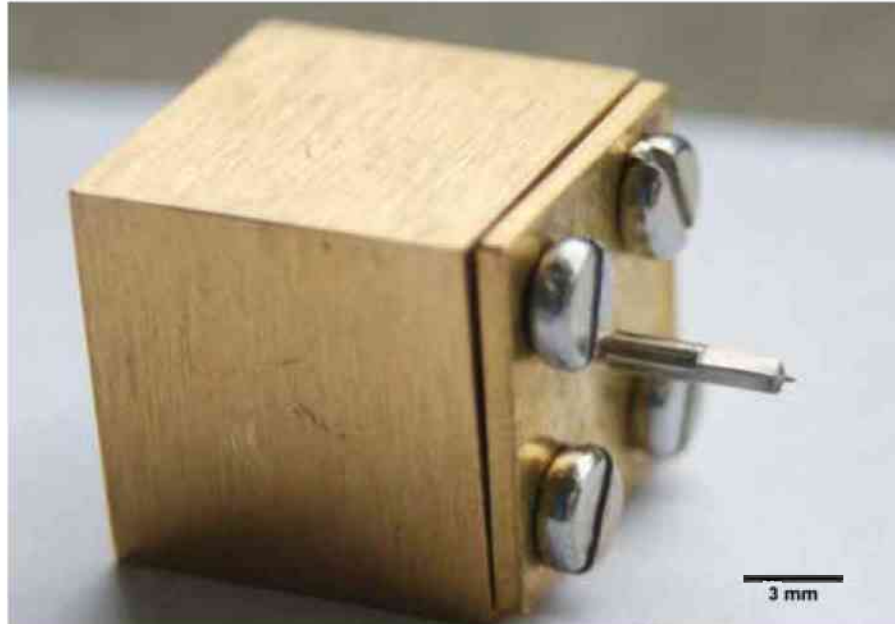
Haltevorrichtung für die Indenterspitze mit angebrachter Wolframnadel zur FIB-Präparation.
